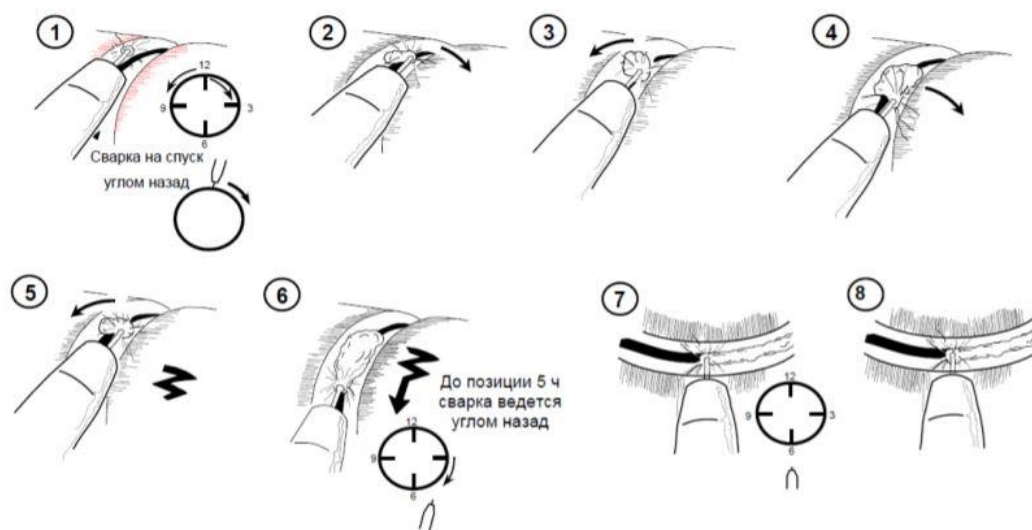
Методика сварки корневого слоя шва методом STT [24]
